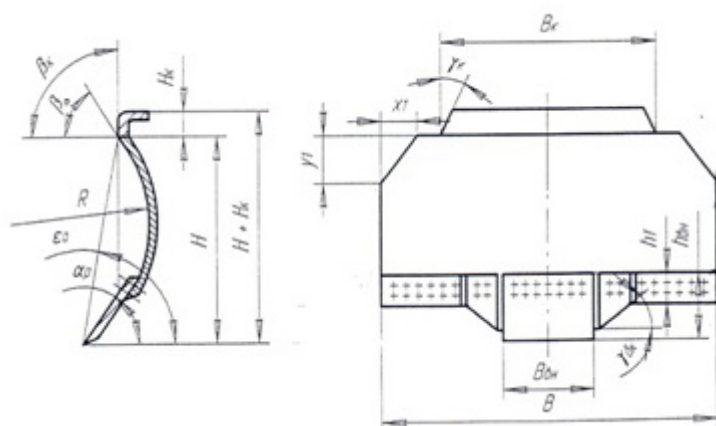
Схема бульдозерного отвала с выступающим средним ножом, боковыми косынками и скосами
